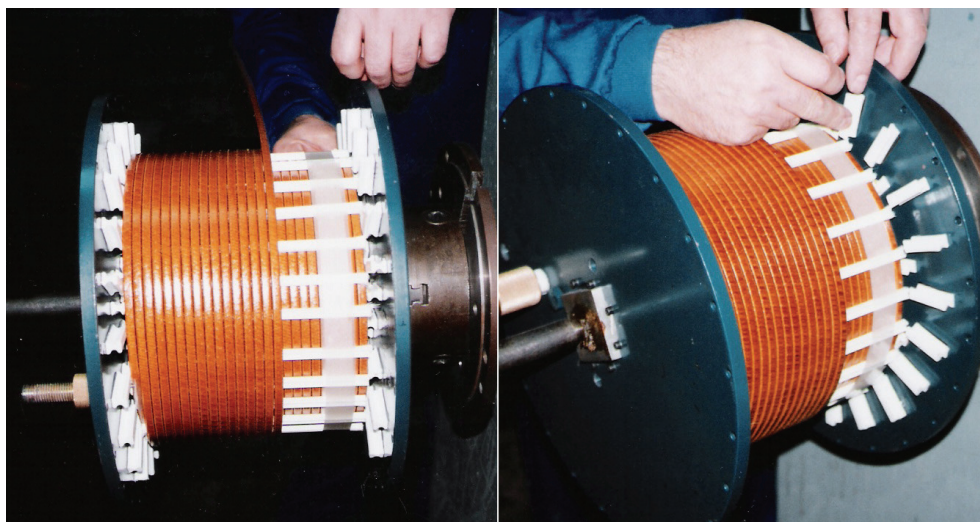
Colocación de los separadores de fibra de vidrio.
